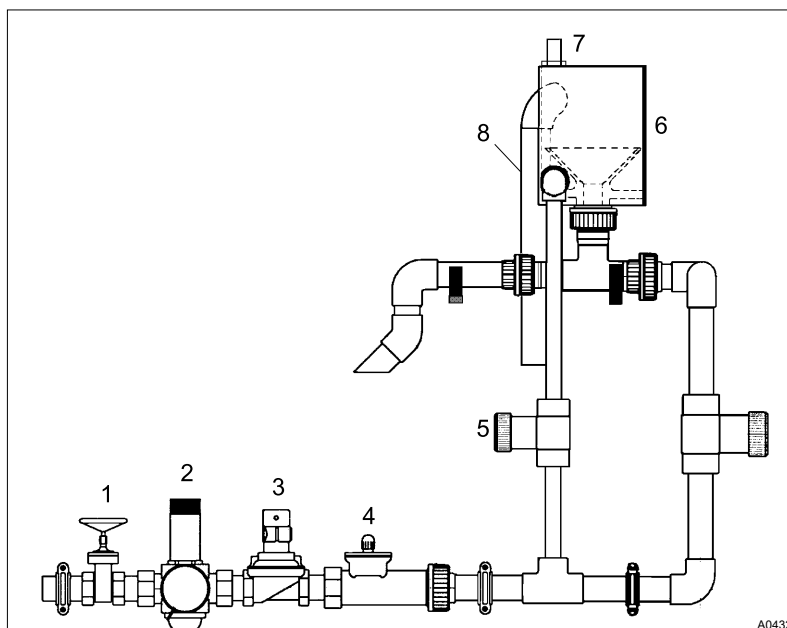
Mecanismo hidráulico con embudo de enjuague
